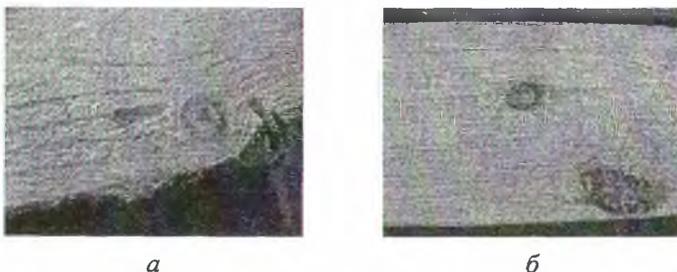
Поверхности пластей бруса древесины сосны, полученные базовыми (а) и разработанными новыми (б) двухлезвийными ножами
